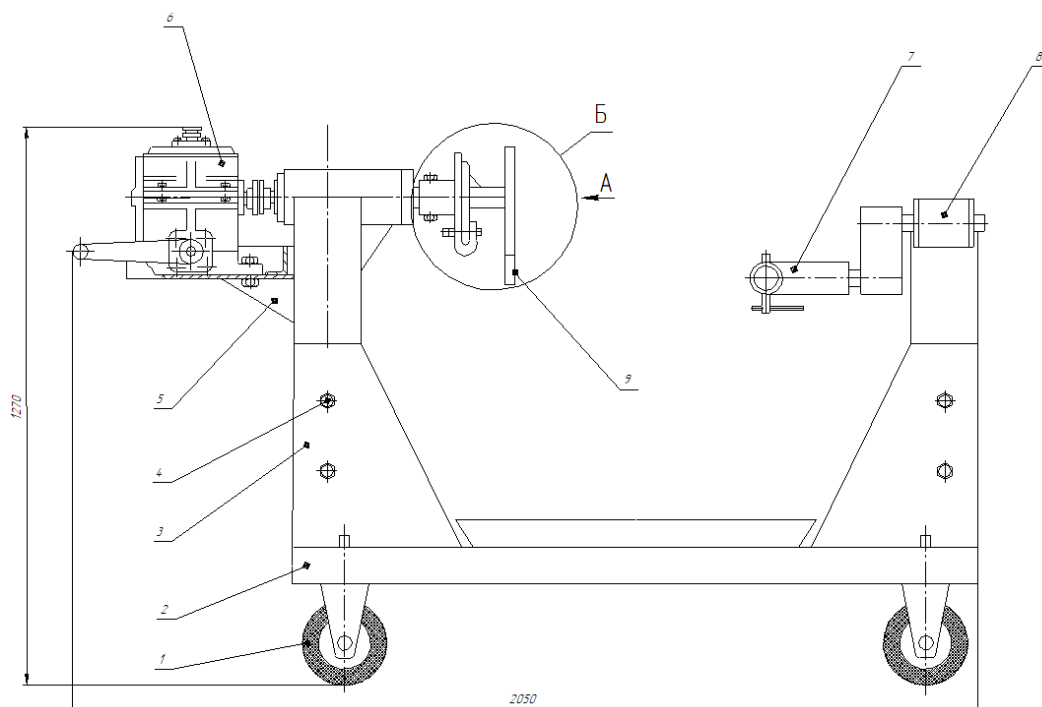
Проектируемая модель стенда для разборки сборки коробок передач
